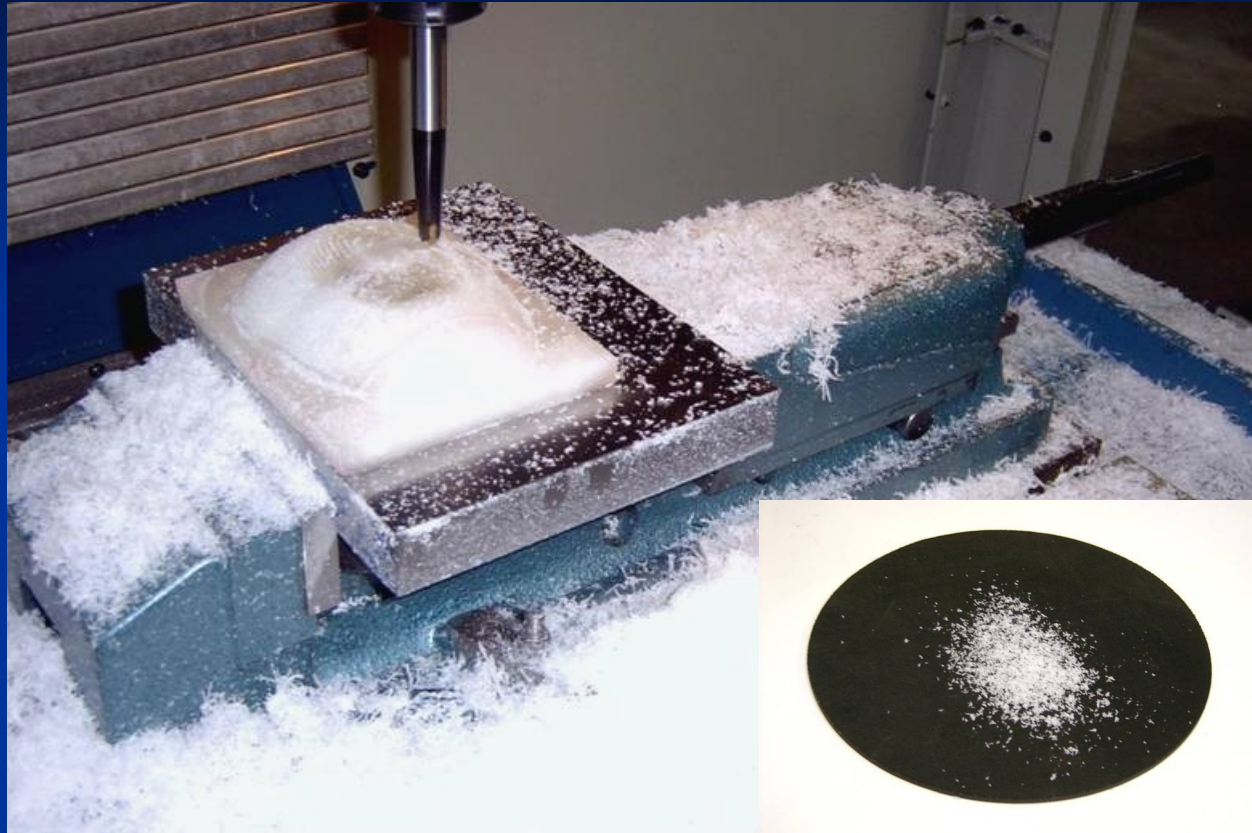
Usinagem da superfície externa: acabamento.
